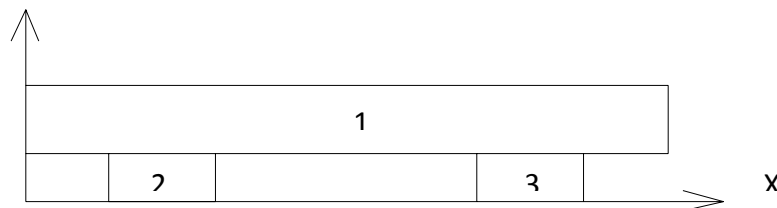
Sección de la llanta y forma en que se divide para el cálculo.
